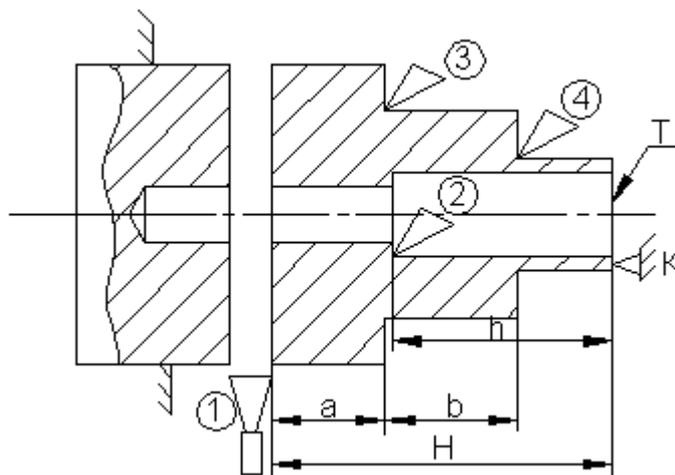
Схема обработки на токарно-револьверном станке.
